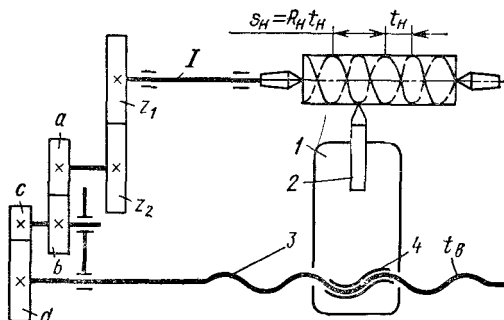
Кинематическая схема резьбонарезной цепи со сменными колесами
